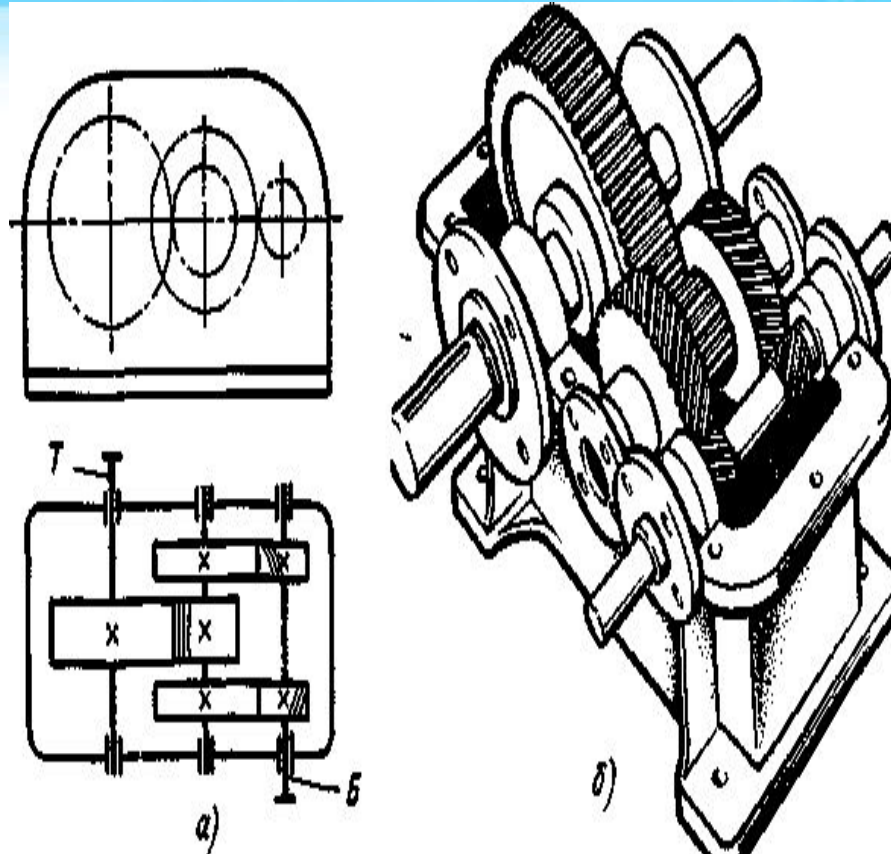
а - Двухступенчатый цилиндрический редуктор с раздвоенной ступенью
